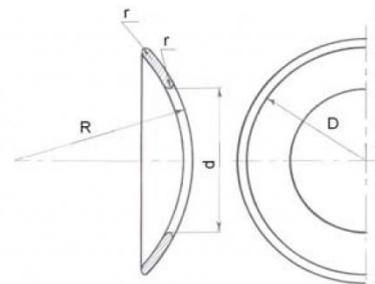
Упругая шайба с квазисферическими торцовыми поверхностями
